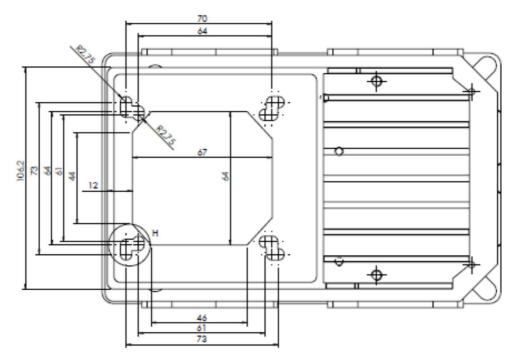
Fixing dimensions for IMTP(D) - ITTP(D) 2.2M fixing type M80T
